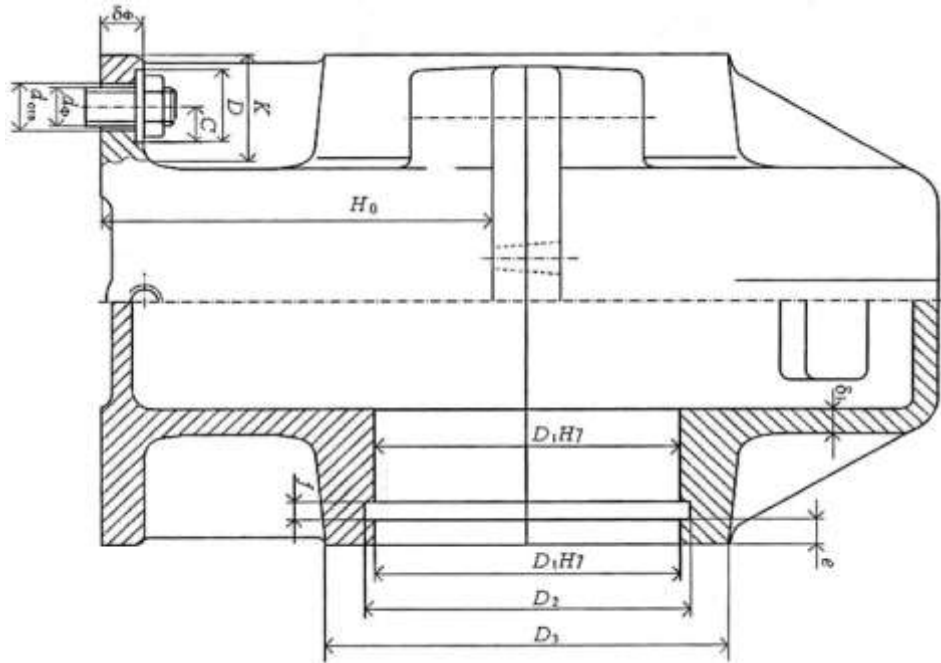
К определению рекомендуемых соотношений размеров корпуса редуктора.
